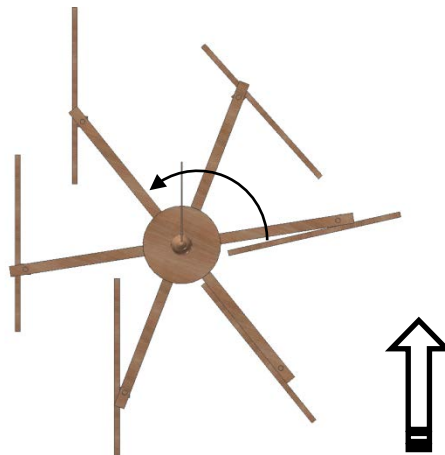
Detalle del mecanismo rotor que produce el movimiento al conjunto.
